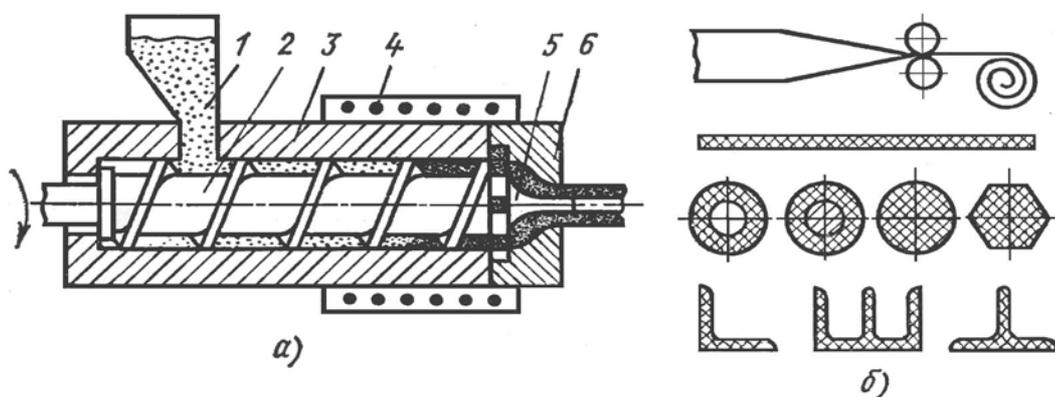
Непрерывное выдавливание (экструзия): а – схема установки; б – профили получаемых деталей
